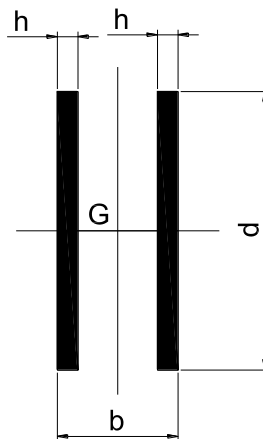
Cordón soldadura anclaje inf. de suspensión
